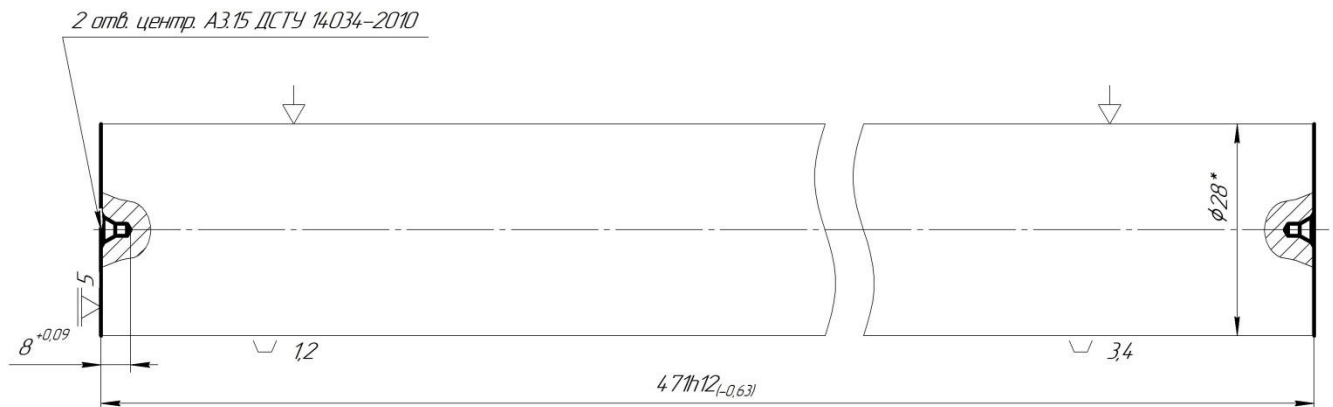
Схема установки заготовки на призми з притиском прихватами
